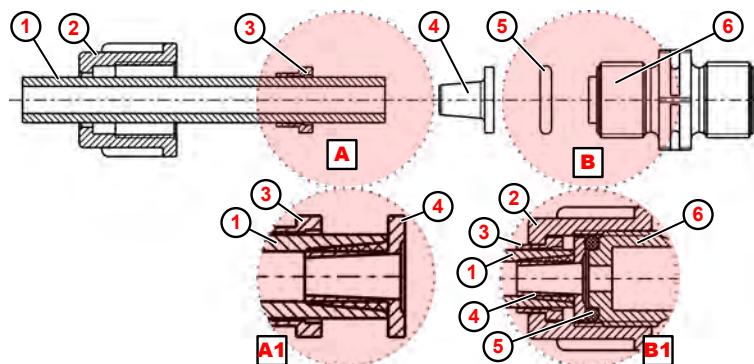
Rohr- Schlauchanschluss mit Kegelteil
